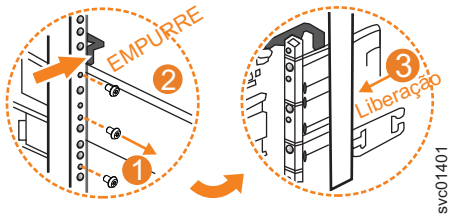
Remova a montagem de trilho do suporte traseiro da estrutura
